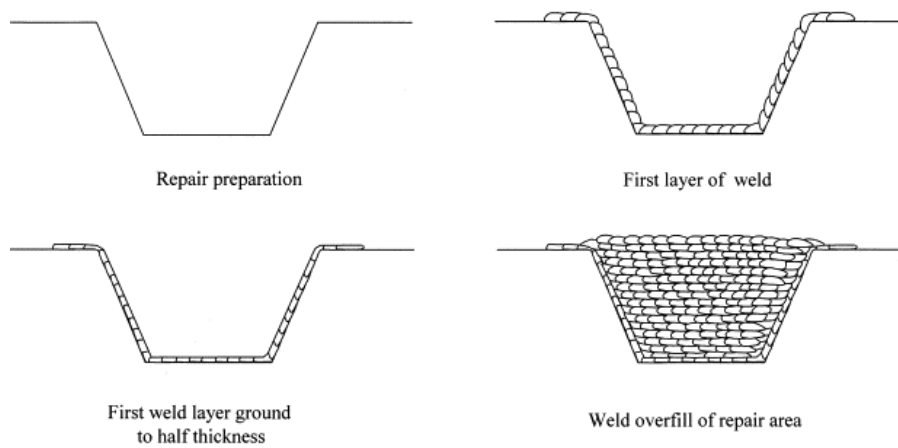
Half-bead weld 覆層銲接處理。
